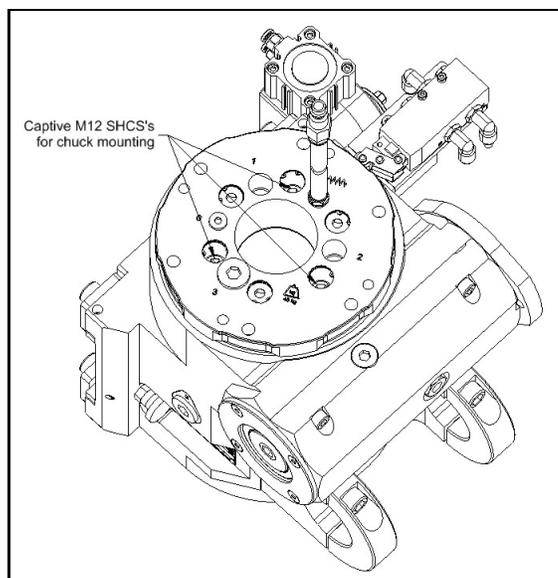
ACOPLAMIENTO DEL ENSAMBLAJE DE AMARRE EXTERIOR AL CUERPO PRINCIPAL
